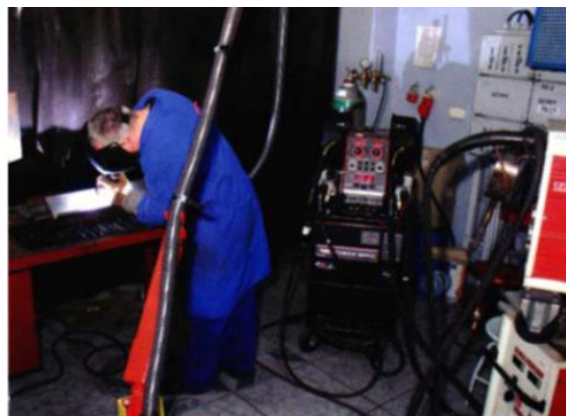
Soldador realizando trabalhos com um suporte com extração dos poluentes. Equipamento fabricado pela Aspirmig, projetado durante o projeto europeu ECONWELD [5,54].
